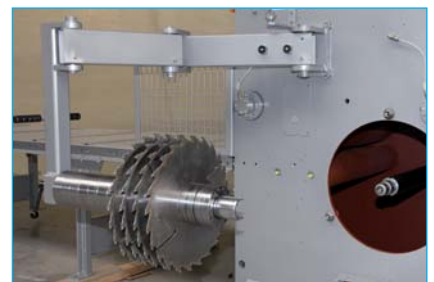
Ausziehen der Sägebüchsen auf einen schwenkbaren Halter (Option) für einen einfachen Werkzeugwechsel.
